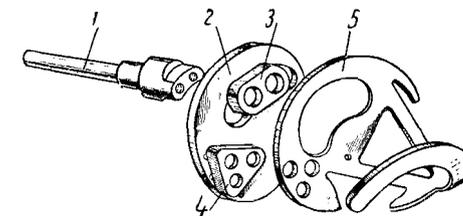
Детали вращающегося нитепритягивателя машины 97-го класса
